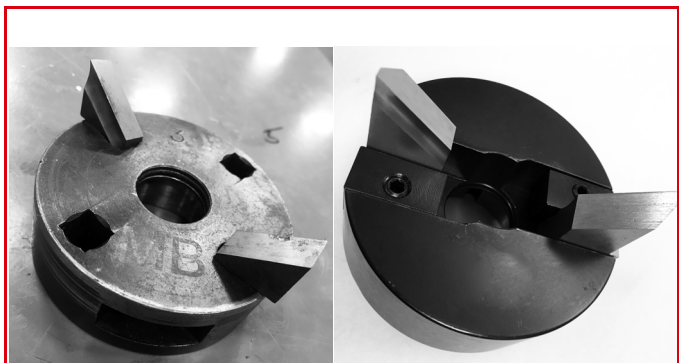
PORTE-OUTILS FIXE (L) ET COULISSANT (R) AVEC EMBOUT DE COUPE.
